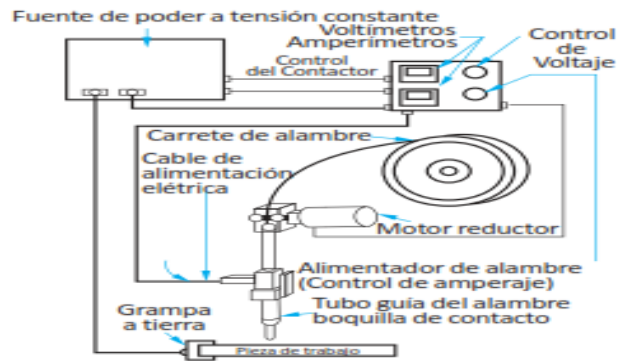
Esquema del Circuito de una soldadora GMAW
